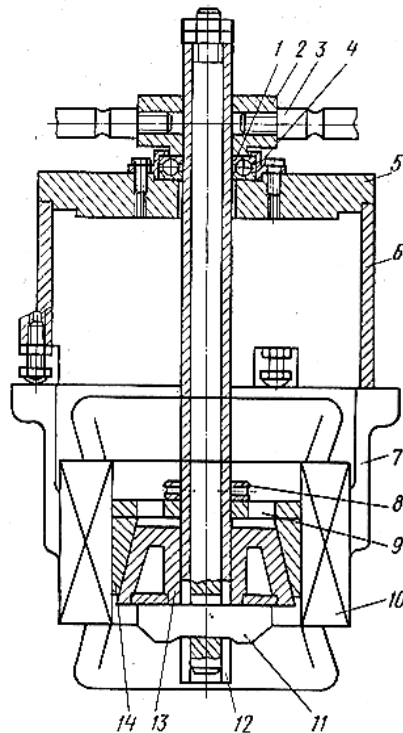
Съемник для выпрессовки статора из блок-картера бессальникового компрессора:
